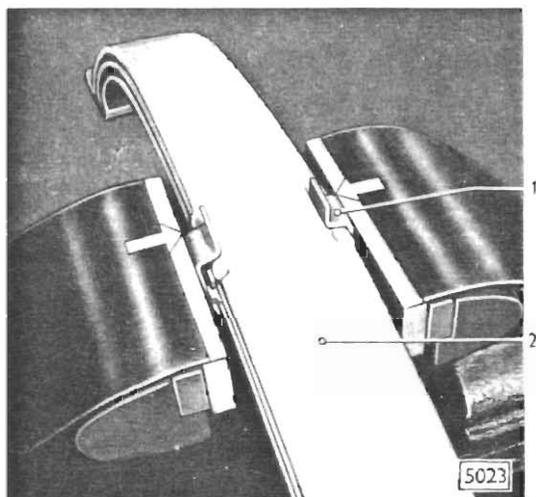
Klammer im Schraubstock um Vorderfeder spannen
